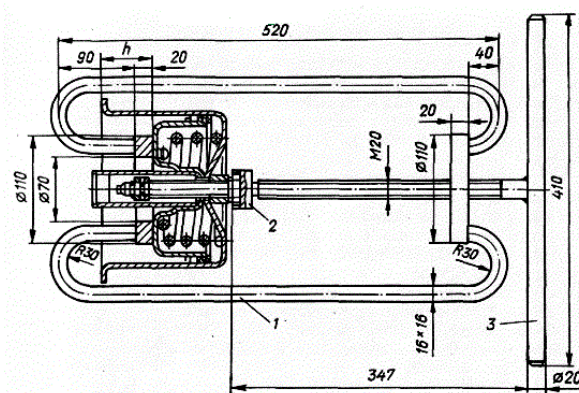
Приспособление для разборки и сборки энергоаккумулятора
